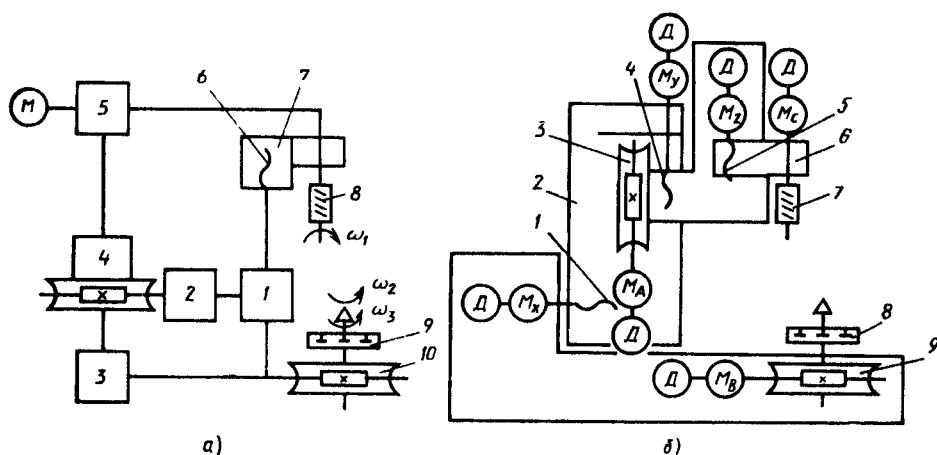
Принципиальная схема зубофрезерного станка:
